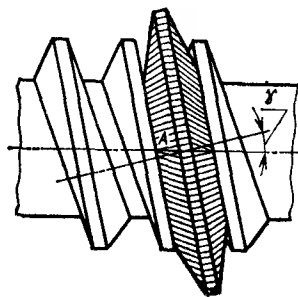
Схема установки резцов для нарезания левого червяка Z1
